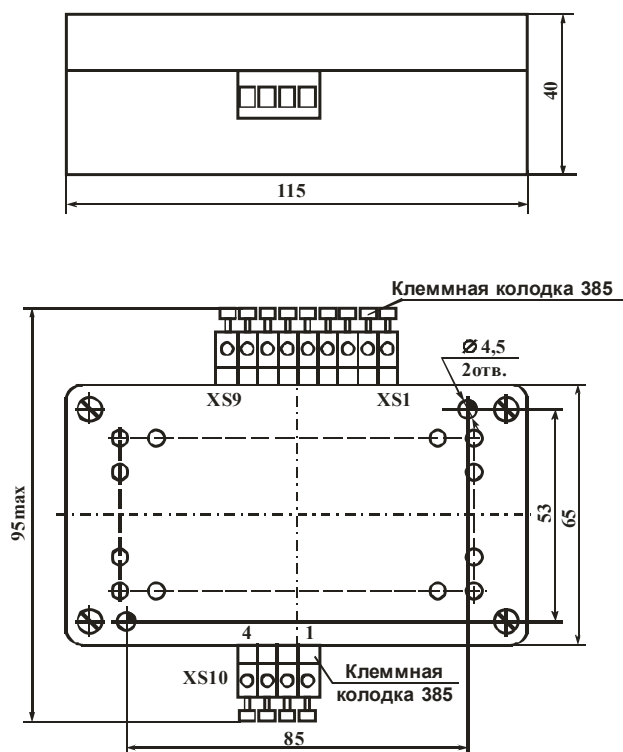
Габаритный чертеж ДТРВ-400-01
